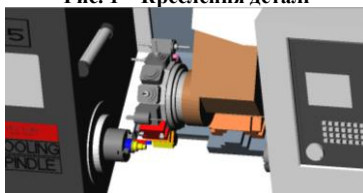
Візуалізація оброблення деталі в CAM Esprit
